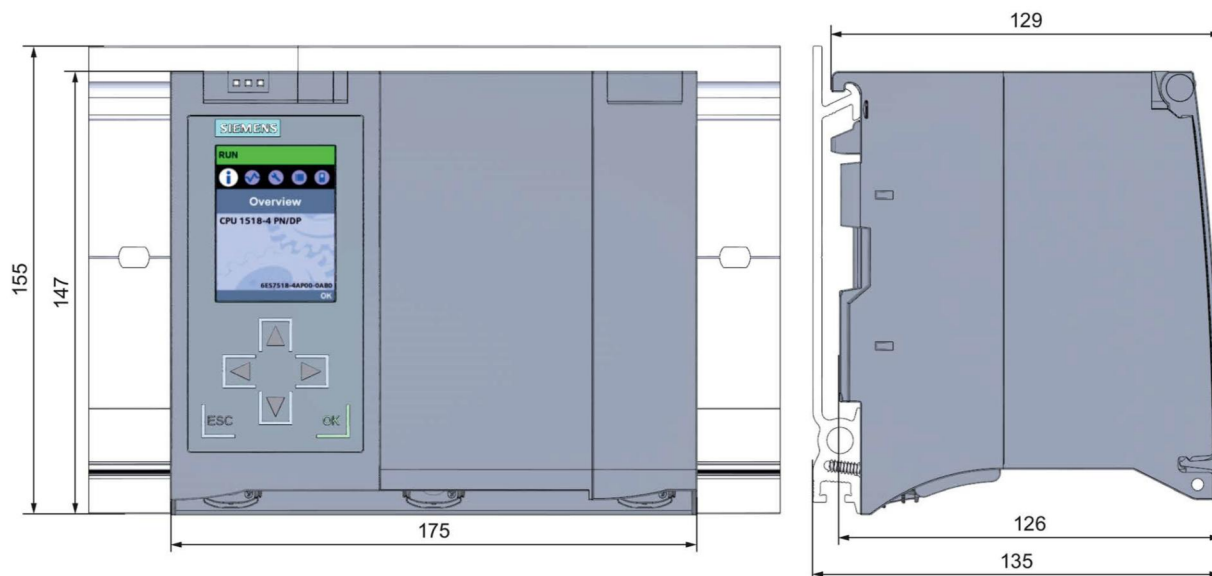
Габаритный чертеж CPU 1518-4 PN/DP, вид спереди и вид сбоку
